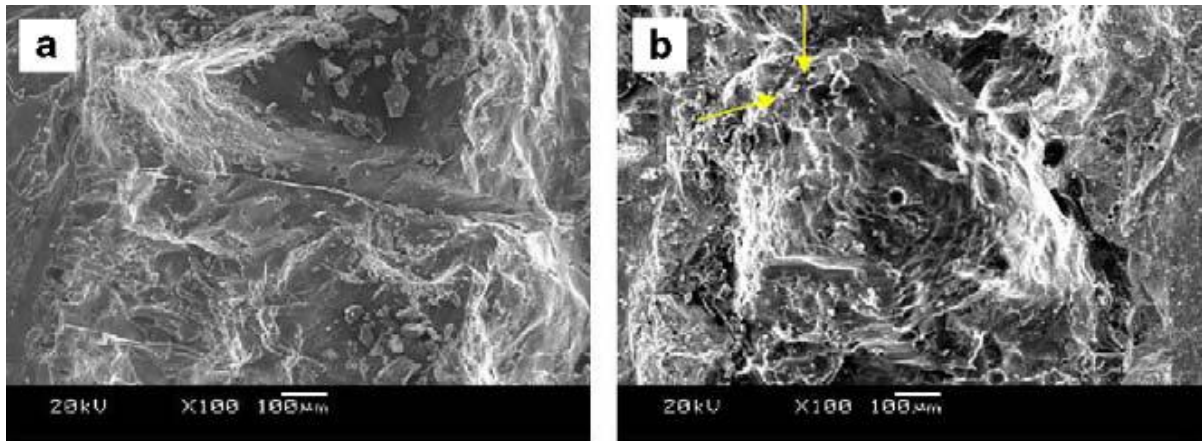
Fractographie d'assemblage : (a) Mg-Al assemblage direct; b) Mg-Al assemblage avec ajout de Ce. [Liu L – 06]
